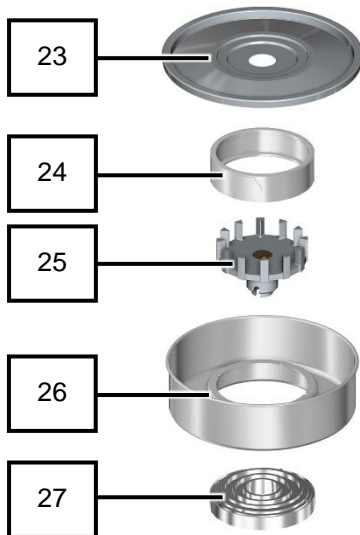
Übersicht Mahlwerkzeuge und Kassette
